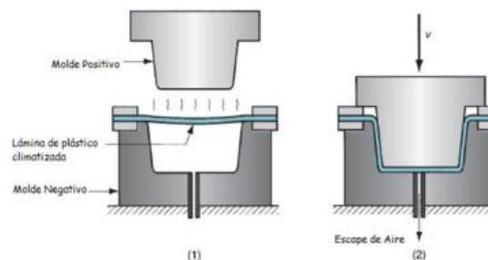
Termoformado mecánico. Fuente: diseño y construcción de una máquina termoformadora [11]
